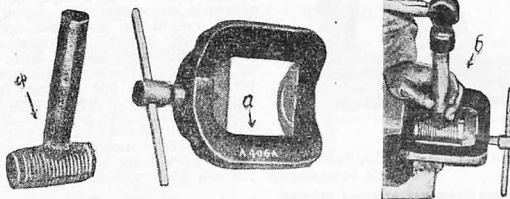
Ф — уплотнитель баббита; а — пресс, зажимающий бортики 3-го подшипника; б — уплотнение баббита в 3-м подшипнике
